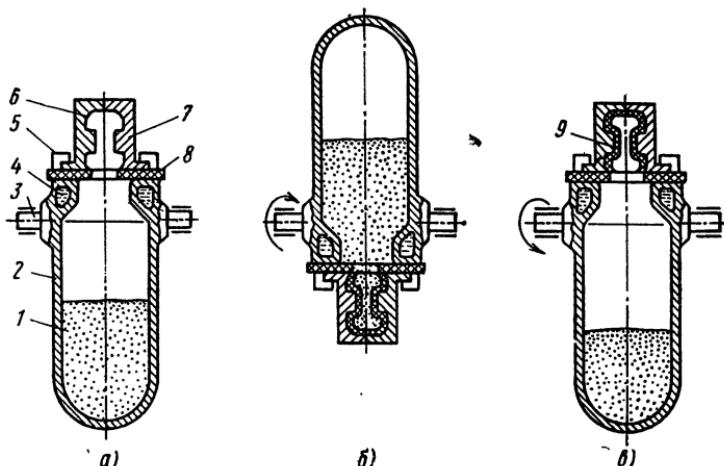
Изготовление оболочкового стержня на установке с поворотным бункером:
